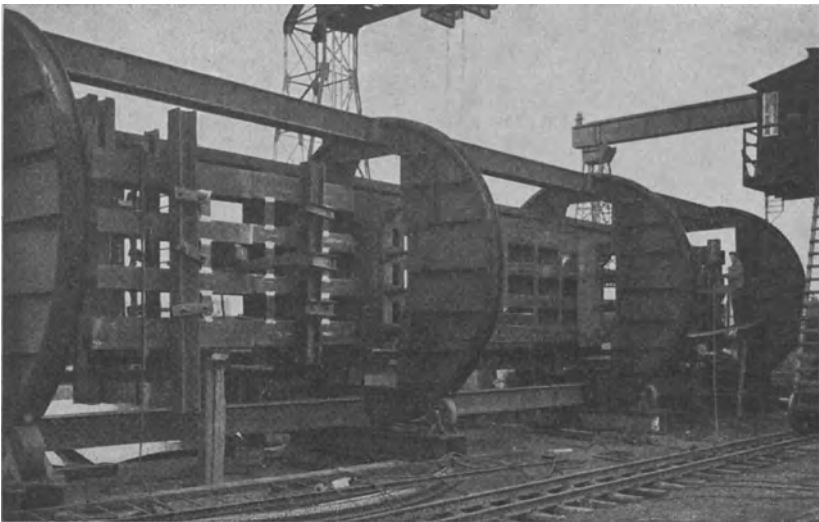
Schweißung einer Tragbrückenkonstruktion in Drehscheiben.
